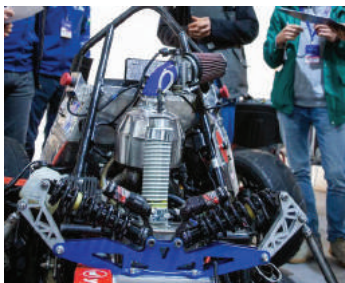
Ресивер изготовленный из алюминия с «банкой»
